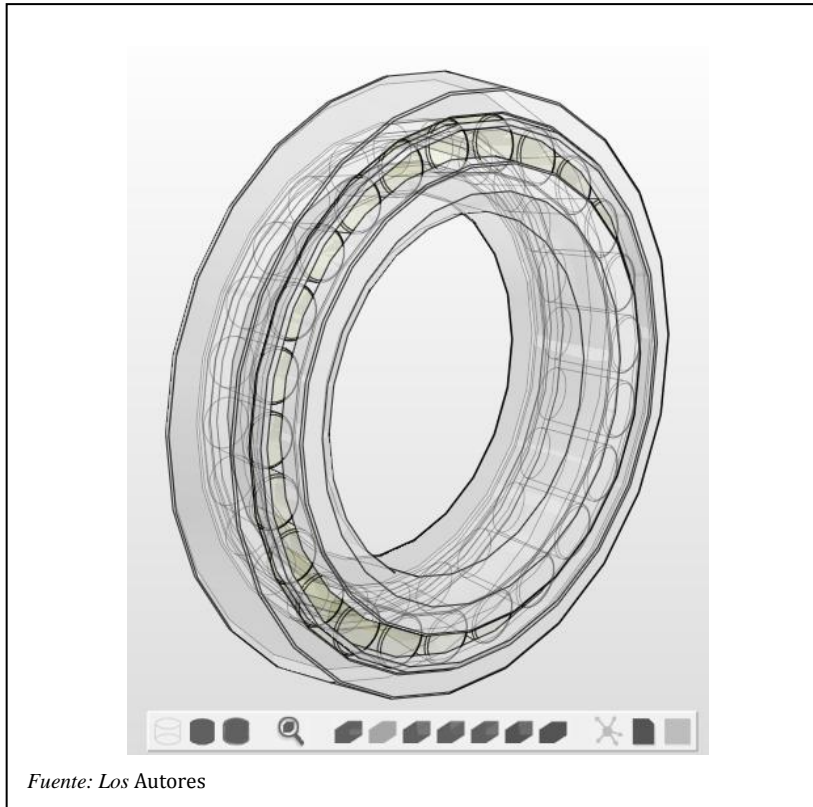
Rodamiento de Rodillos Cónicos Seleccionado (2)
